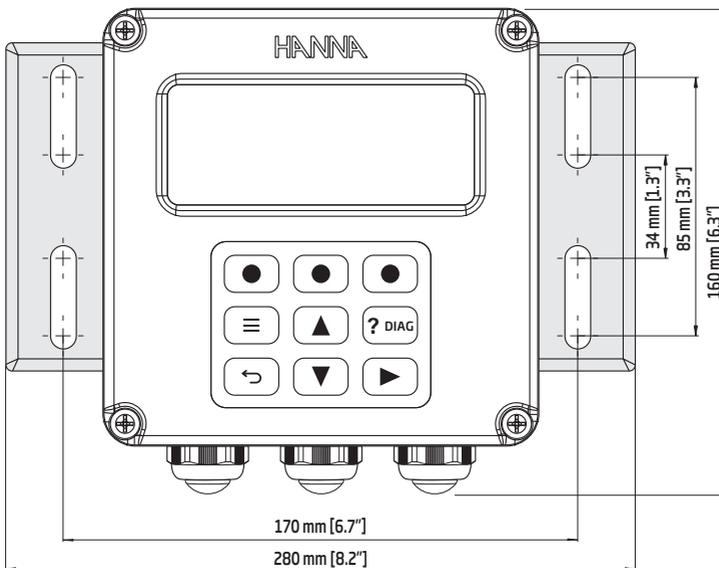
Panel de Montaje en Pared, Dimensiones de las Ranuras
